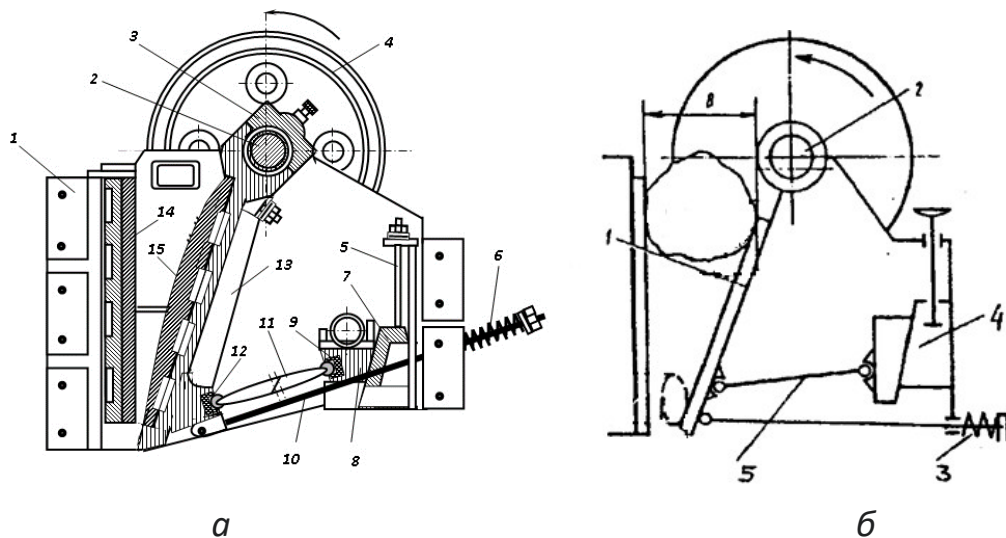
Щокова дробарка зі складним рухом щоки: а- конструкція: 1 –нерухома щока; 2 –ексцентриковий вал; 3 –корінні підшипники; 4 –шків; 5 –гвинт; 6 –пружина; 7 –клин; 8 –упор; 9,12 –вкладиші; 10 –тяга; 11 –розпірна плита; 13 –рухома щока; 14,15 –змінні футерувальні плити; б –схема: 1 – рухома щока; 2 –ексцентриковий вал; 3 –пружина; 4 –клин; 5 –розпірна плита;
